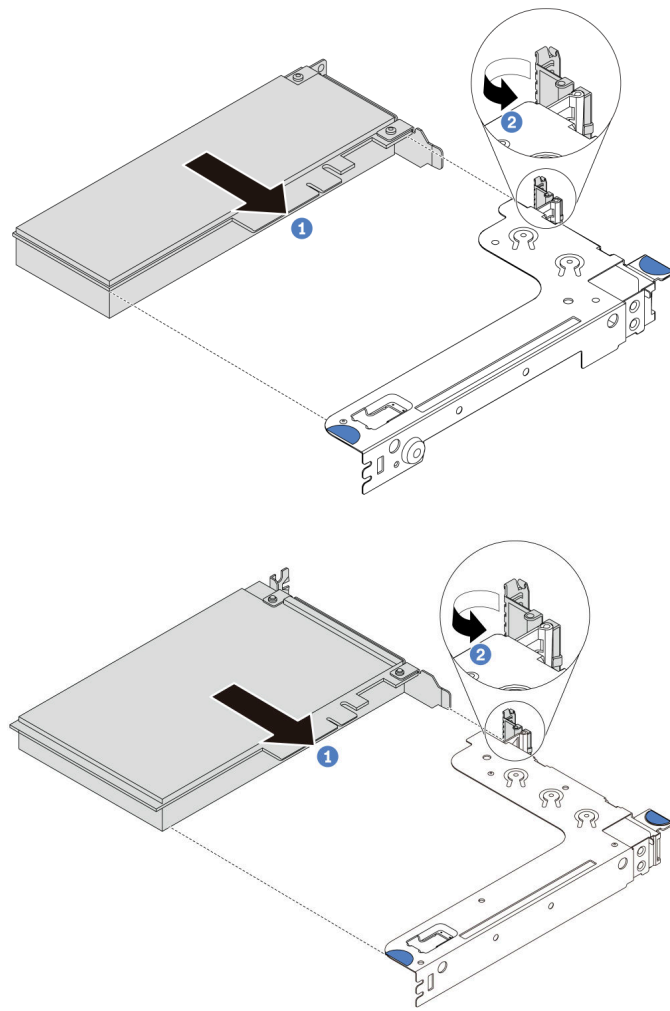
Instalação do conjunto de placa riser 1 (LP/FHFL)
